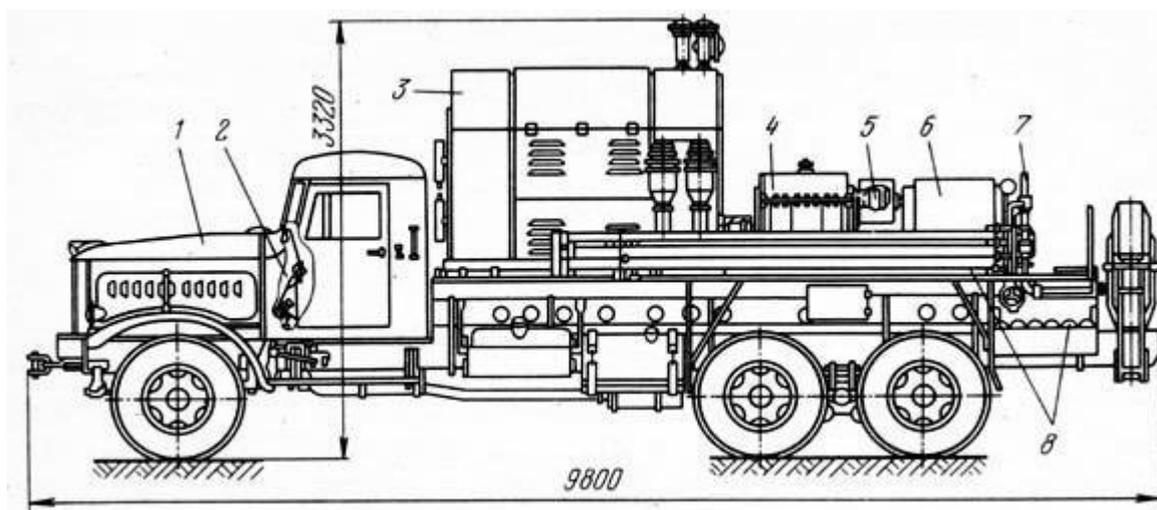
Насосный агрегат 4АН-700 для ГРП: 1 – автомобиль КрАЗ-257; 2 – кабина управления; 3 – силовой агрегат; 4 – коробка скоростей; 5 – муфта сцепления; 6 – насосный агрегат; 7 – выкидной маинфольд; 8 – соединительные трубы высокого давления
